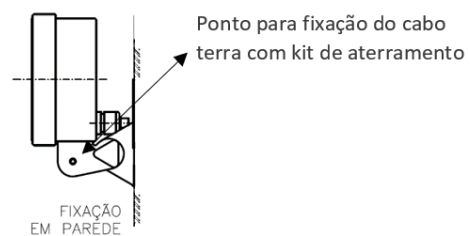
Linha 3100D detalhe local fixação terra com suporte em parede
